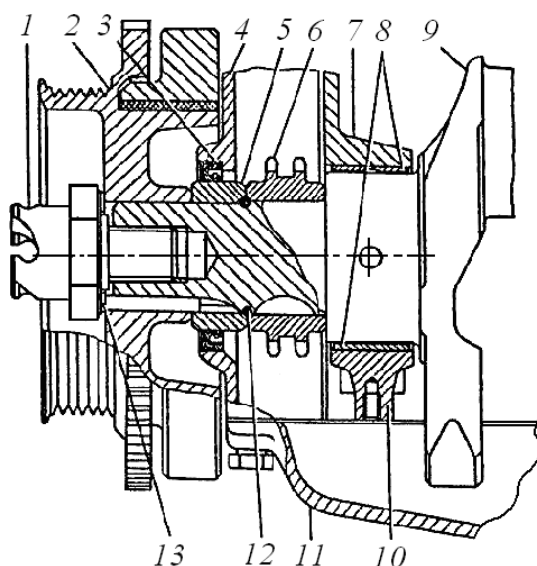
Передний конец коленчатого вала: 1 – храповик (или болт); 2 – шкив-демпфер с диском синхронизации; 3 – манжета; 4 – крышка цепи; 5 – втулка; 6 – звездочка; 7 – блок цилиндров; 8 – вкладыши подшипника; 9 – коленчатый вал; 10 – крышка подшипника; 11 – масляный картер; 12 – резиновое уплотнительное кольцо; 13 – стопорная шайба храповика
